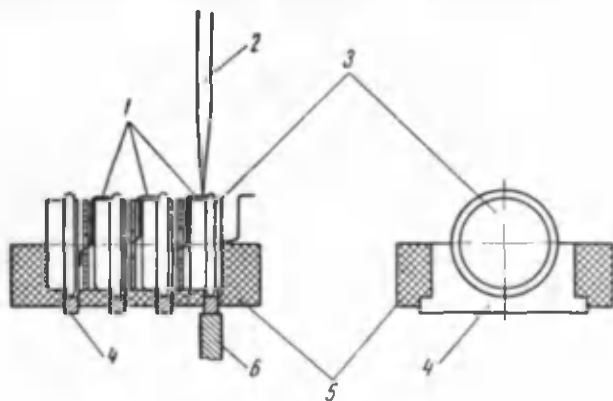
Приспособление для точечной сварки ртутно-цинковых элементов:
